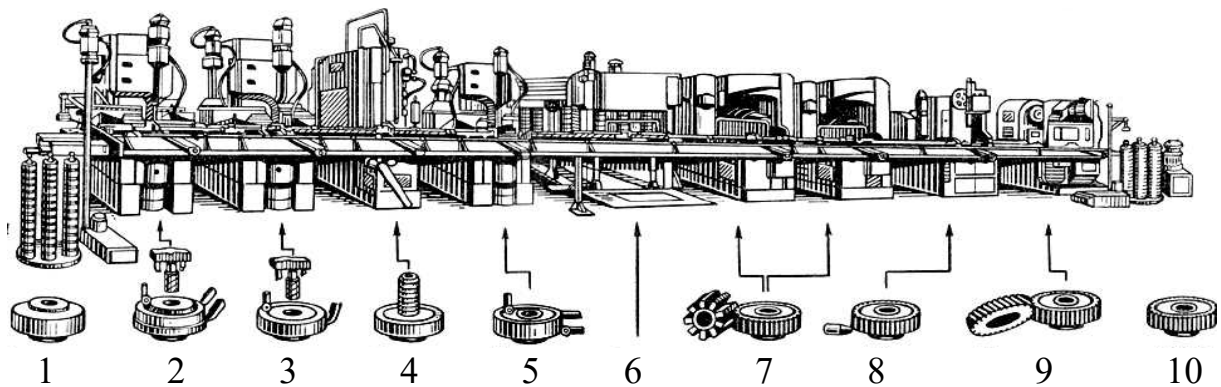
Схема автоматичної лінії для виготовлення деталі типу «зубчасте колесо» (зверху) та схеми обробки на ній заготовки (внизу): 1 – заготовка; 2, 3 – перша й друга токарна й фрезерна операції; 4 – протягування; 5 – чистова токарна операція; 6 – бункер; 7 – фрезерування; 8 – зубозаокруглення; 9 – зубошевінгування; 10 – деталь
